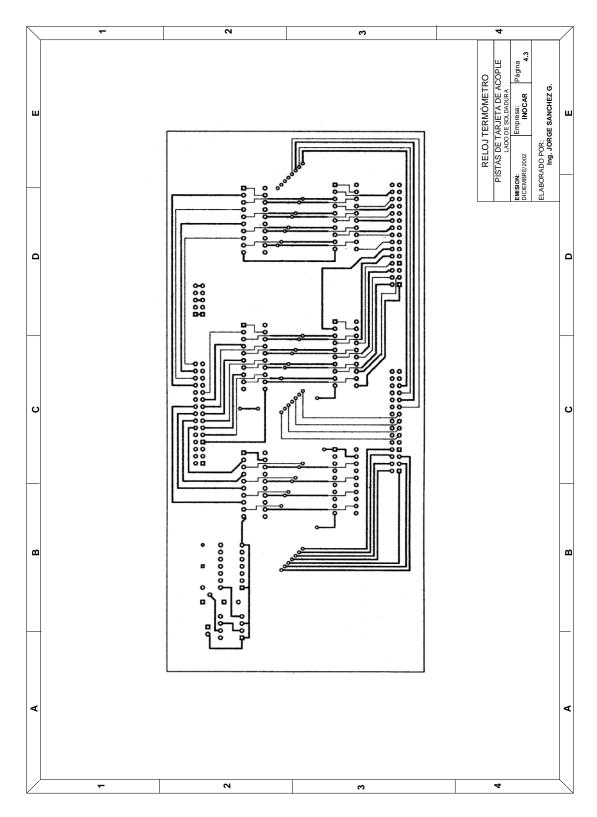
Tarjeta de acople (Pistas lado de soldadura)
